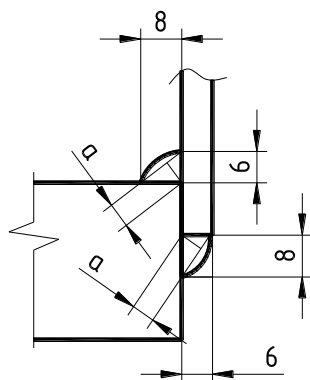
Схема сварных швов соединения опорной стойки (пояса) с фланцем
